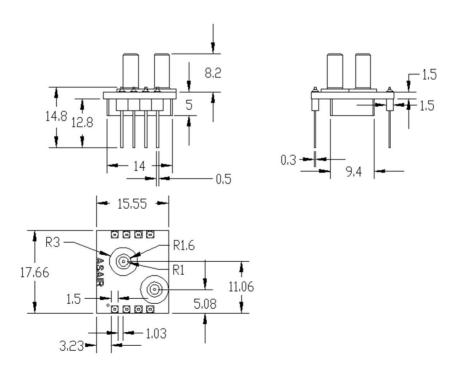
尺寸图 (单位: mm, 未标注公差: ±0.2mm)
